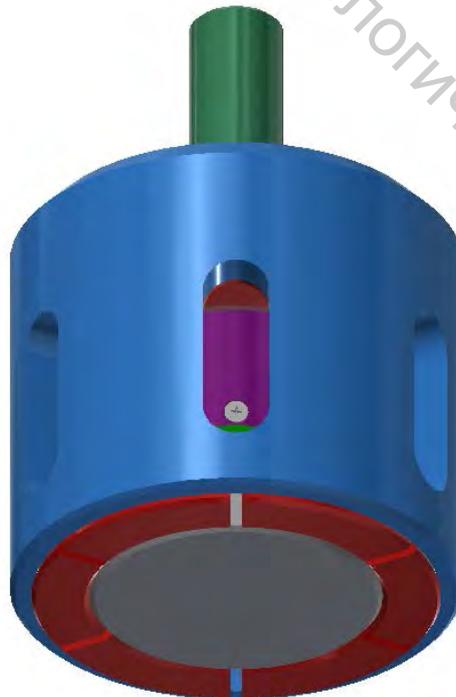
Головка пневматического патрона для зажима кольца по наружной поверхности
